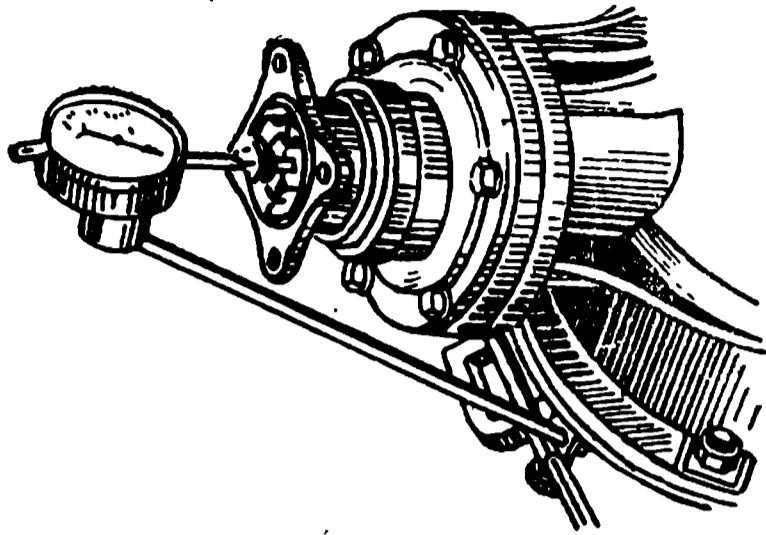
Определение осевого люфта в подшипниках вала ведущей шестерни главной передачи индикатором
